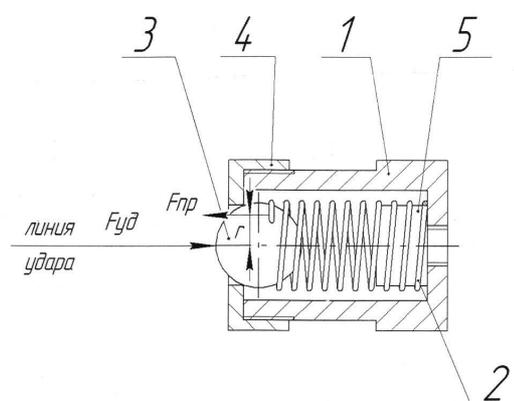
Устройство для квазипластического удара с цилиндрической пружиной 1 – направляющая; 2 – пружина со смещением относительно линии удара; 3 – шар- боек; 4 – корпус; 5 – крепление
